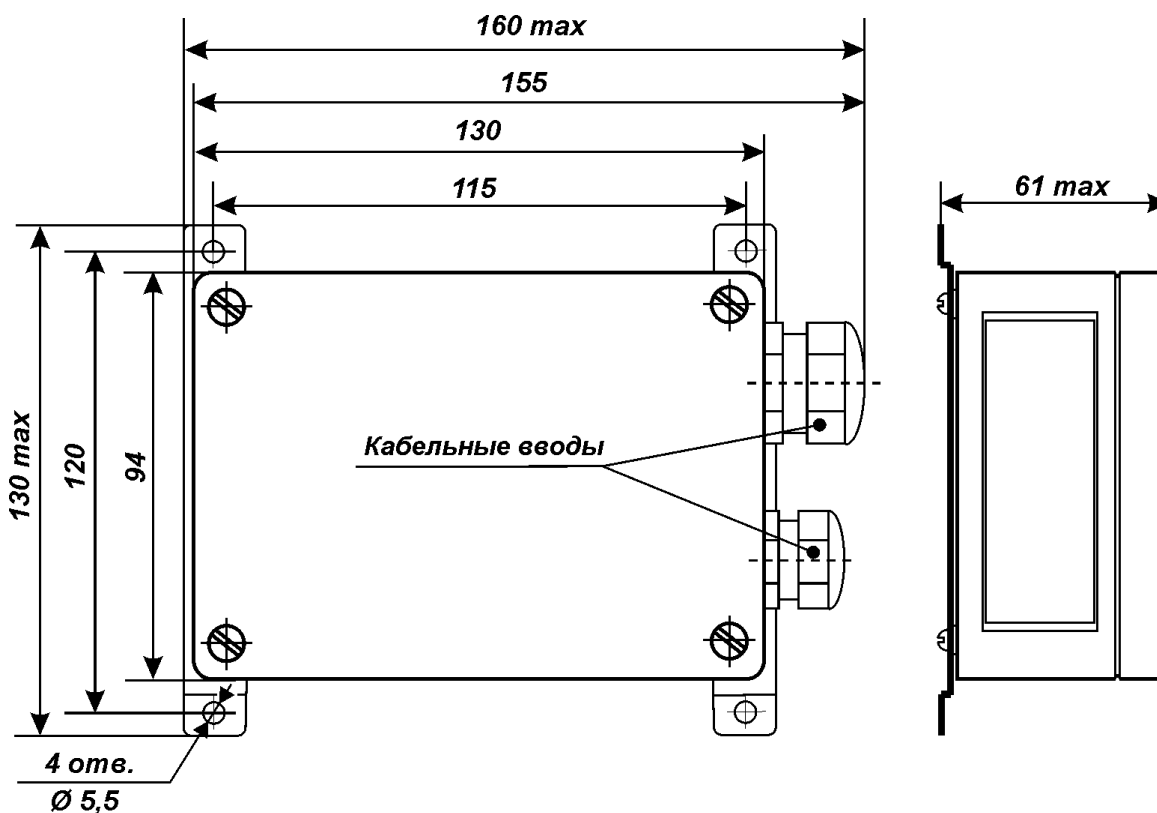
Внешний вид и габаритные размеры ПК-10-1
